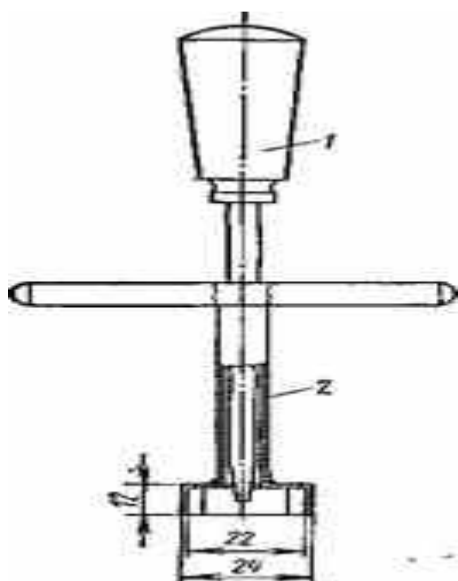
Инструмент для регулировки клапана второй ступени редуктора:
